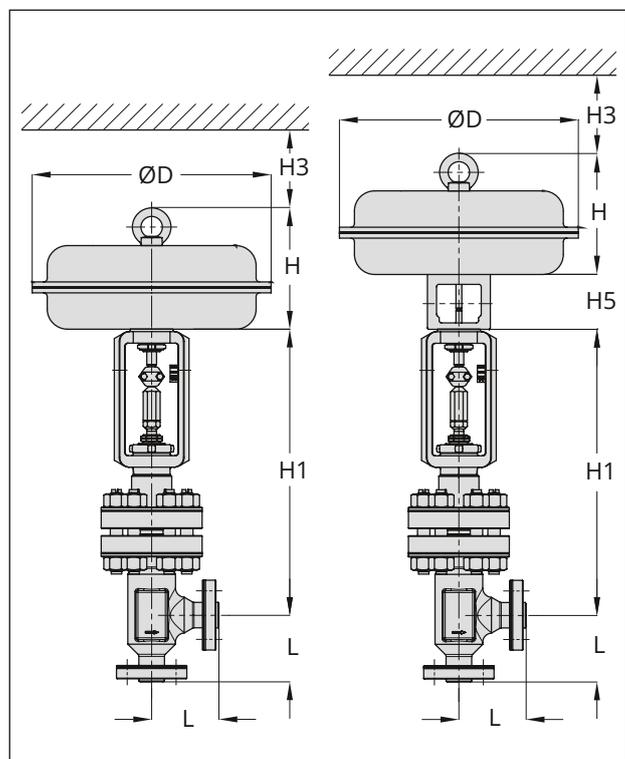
Typ 3259-1 (links) · Typ 3259-7 (rechts)
